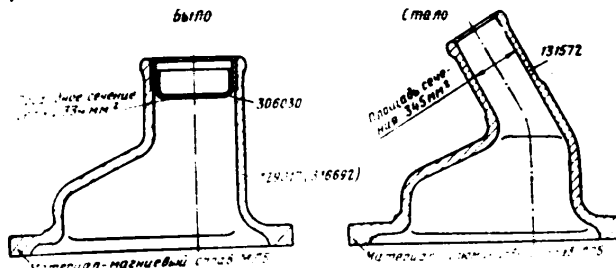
Сечение заднего корпуса нагнетателя по втулкам для заготовки фрикционной муфты.
